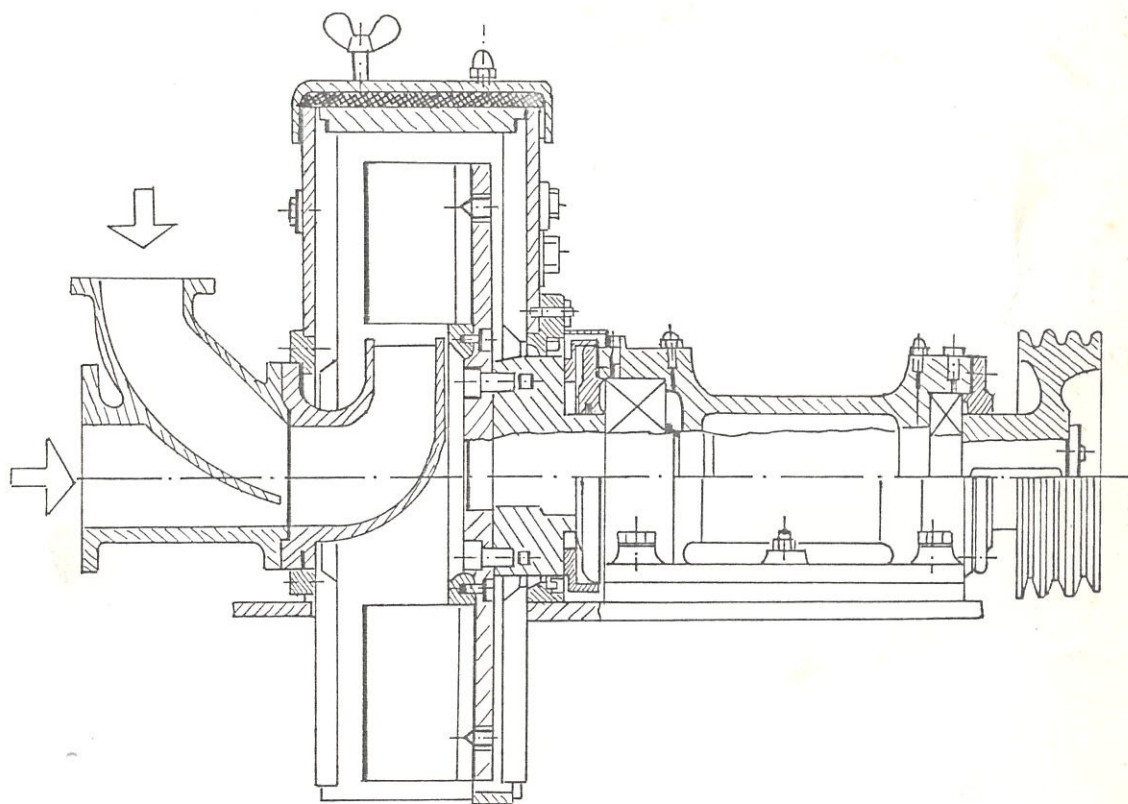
TURBINA TIPO DESLIZADORA DE UNICO DISCO
